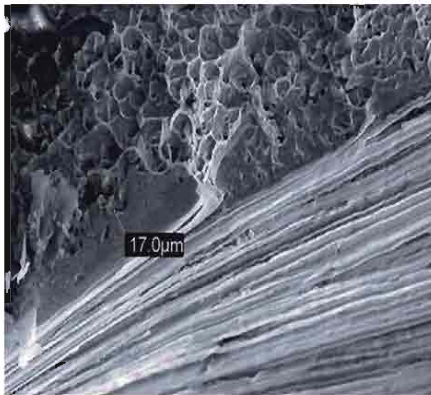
Fracture à partir d'une strie d'usinage
